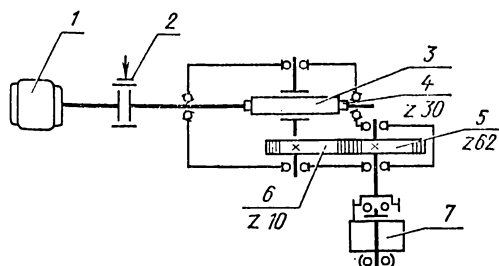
Кинематическая схема стреловой лебедки крана КС-4362:
